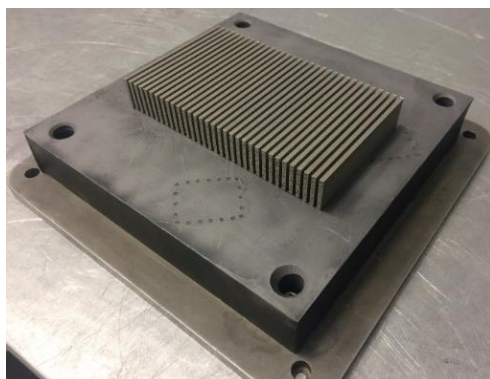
Изготовление образцов для подбора оптимального режима сплавления порошкового материала марки Inconel 738
